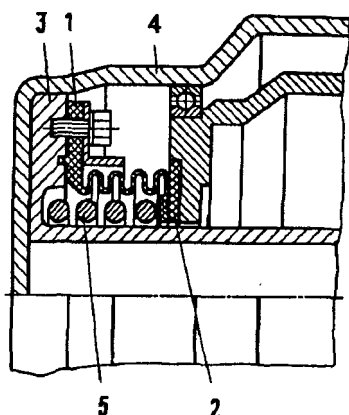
Торцово-силиконовое уплотнение: 1 — силифон; 2 — опорная шайба; 3 — вал; 4 — корпус; 5 — пружина
